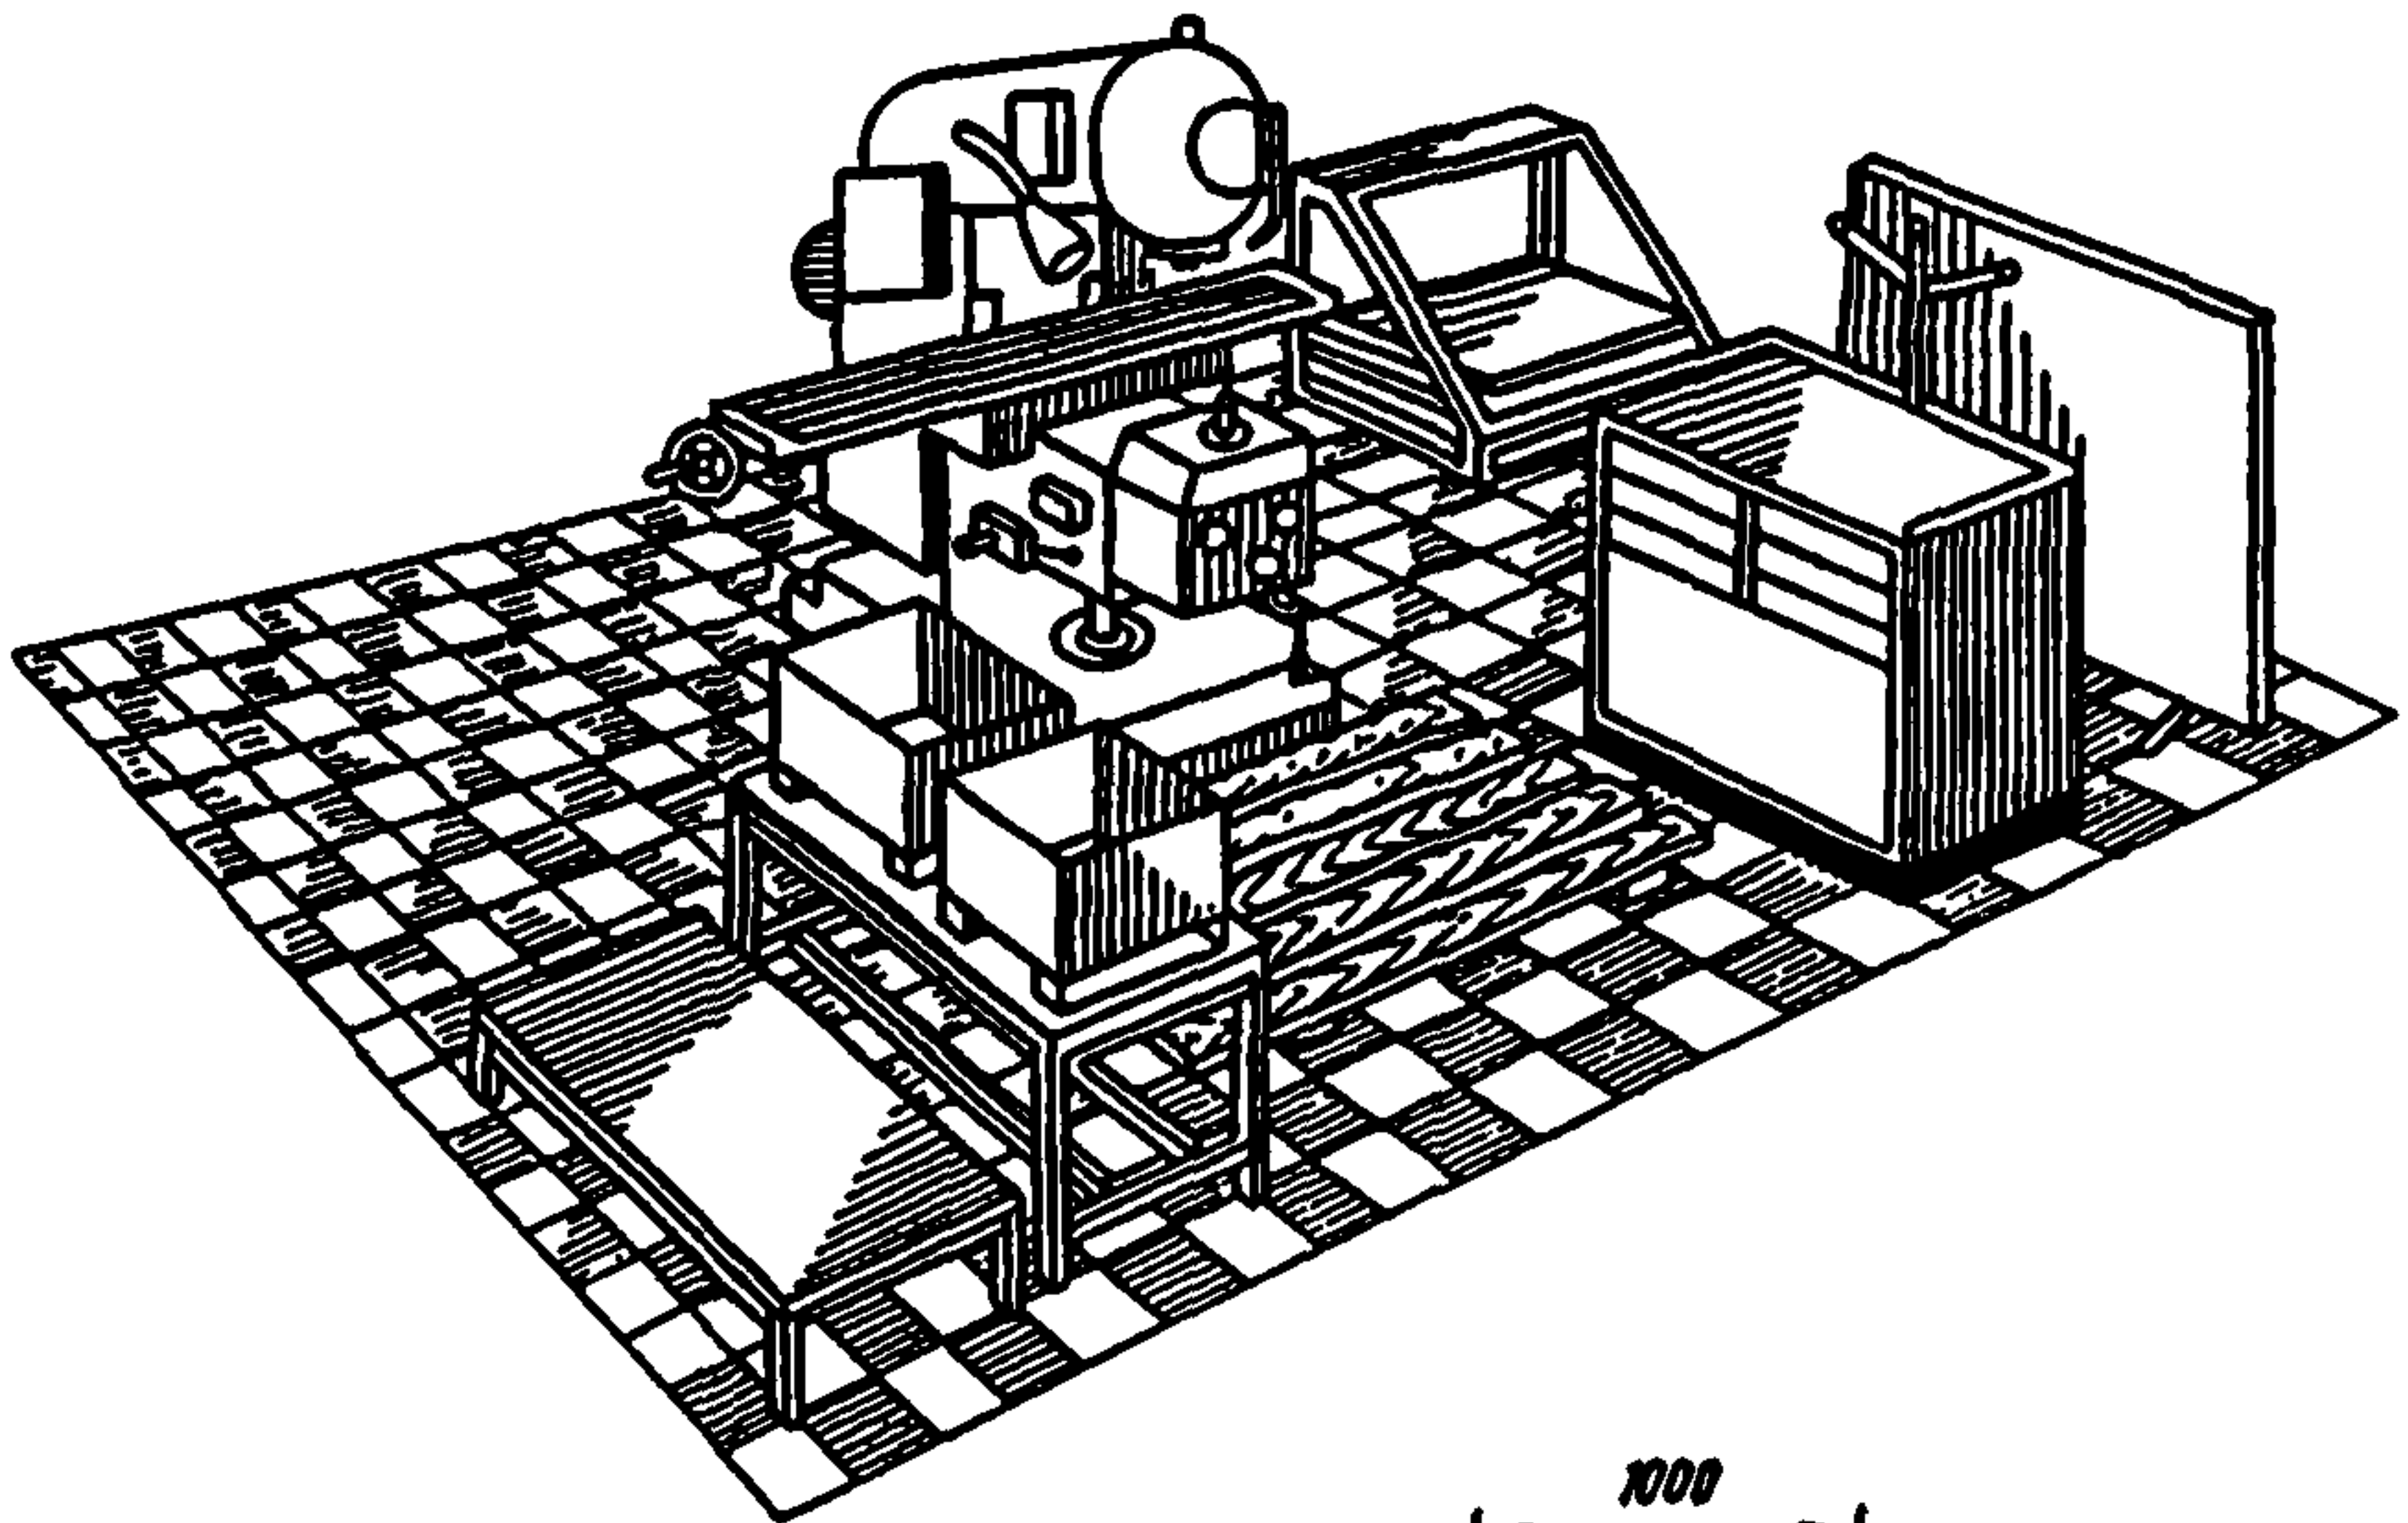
1 — Столик с инструментальными ящиками. 2 — Стол производственный СД3702.51. 3 — Стеллаж для приспособлений СД372501А. 4 — Стеллаж-подставка СД3702.10А. 5 — Тара производственная. 6 — Планшет для чертежей СД3750.04. 7 — Щит экранный. 8 — Решетка под ноги рабочему
